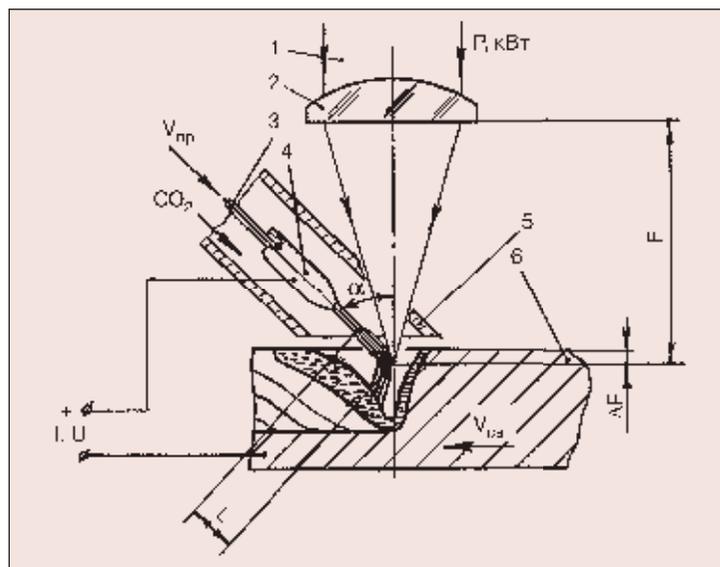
Схема гибридной сварки лазерным излучением и дугой плавящегося электрода с защитой углекислым газом: 1 — лазерное излучение; 2 — фокусирующий объектив; 3 — медный токоподводящий мундштук; 4 — присадочная проволока; 5 — защитное сопло; 6 — образец ($V_{св}$ — скорость сварки, м/ч; $V_{пр}$ — скорость подачи присадочной проволоки, м/ч; ΔF — заглупление горловины каустики излучения относительно поверхности образца, мм; α — угол наклона электрода к оси лазерного пучка, ...°; L — длина дуги, мм; I — сила тока дуги, А; U — напряжение дуги, В)
